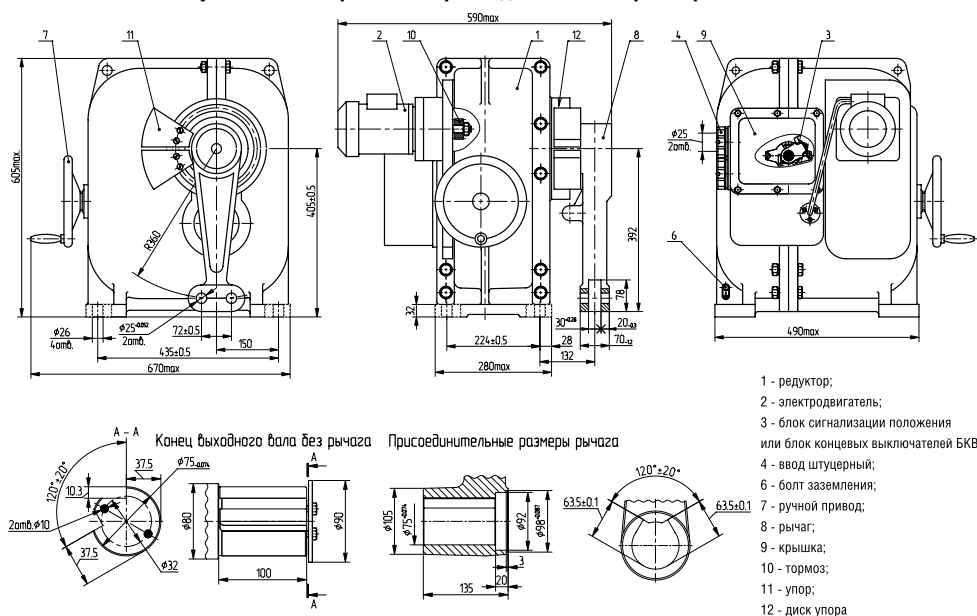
Габаритные и присоединительные размеры М30-630 (1600)-08К
